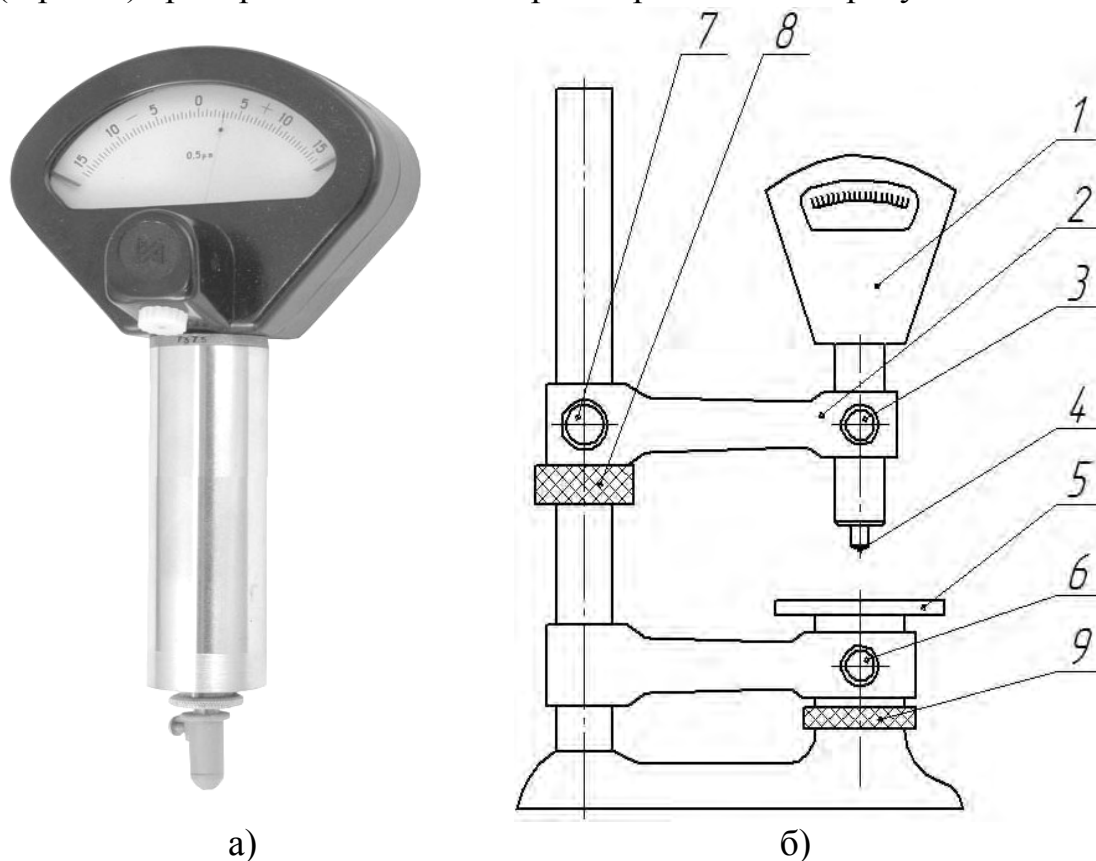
Измерение на микрокаторе: а – общий вид прибора;
